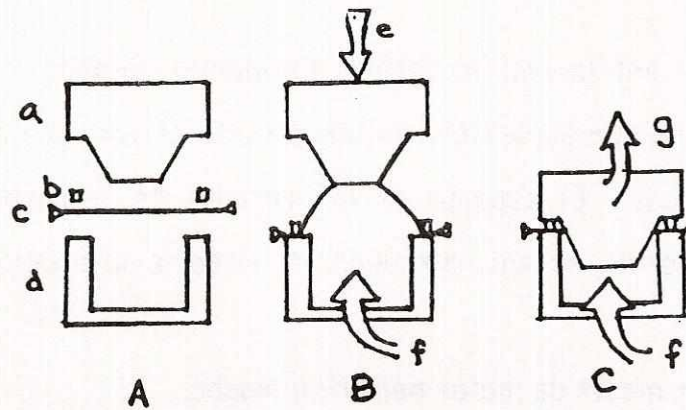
Formado por ondulación y entapizado. A: Lámina precalentada previo al formado. B: Ondulación formada, molde macho penetra la burbuja. C: Formación de la pieza en molde macho por medio de vacío y presión de aire. a: Molde macho con orificios de vacío. b: Anillo sujetador. c: Lámina precalentada y sujeta. d: Cajón de presión. e: Molde macho en movimiento. f: Presión de aire. g: Vacío
